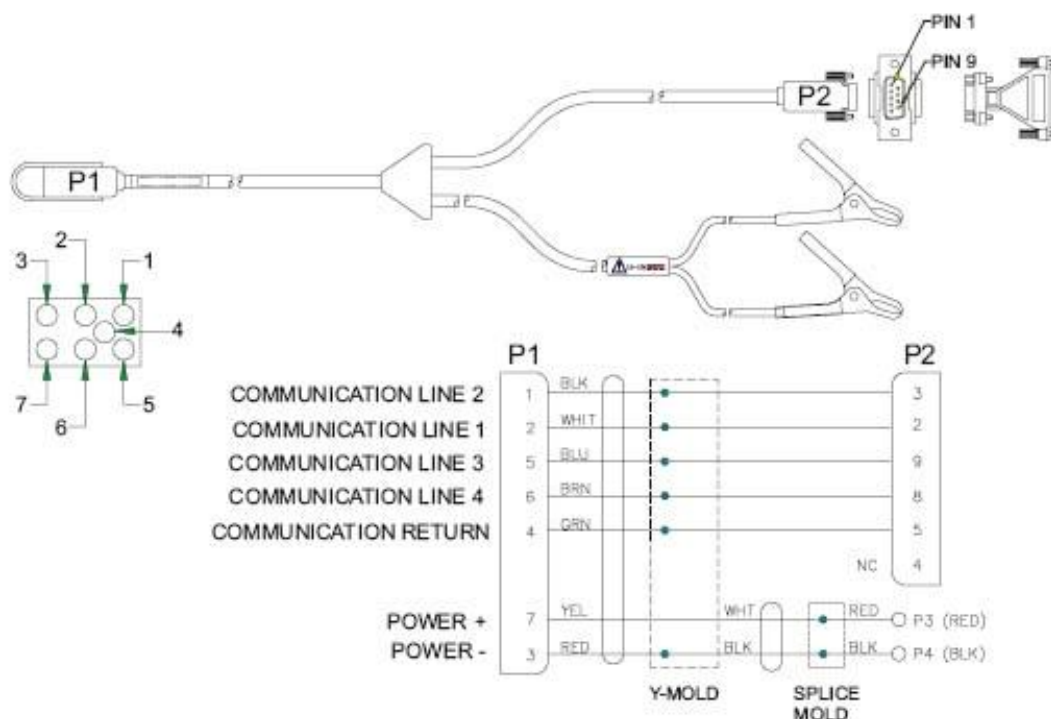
Общий вид и схема соединения кабеля ввода-вывода RS232/RS422
